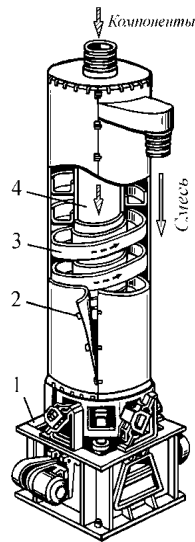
Подъемный винтовой вертикальный вибрационный смеситель: 1 – корпус вибропривода; 2 – съемный кожух; 3 – рабочий орган; 4 – пустотелая колонна (загрузочный бункер)
